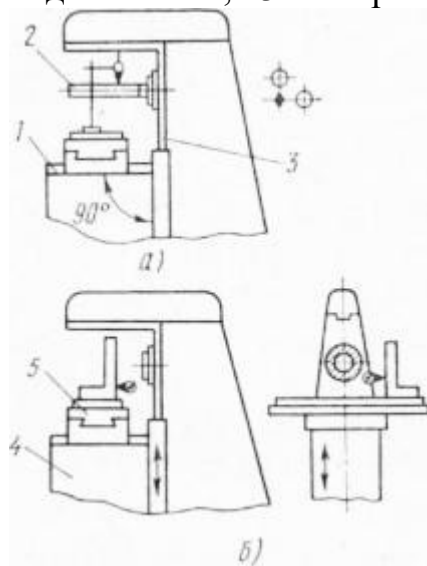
Проверка направляющих консоли на собранном фрезерном станке:
